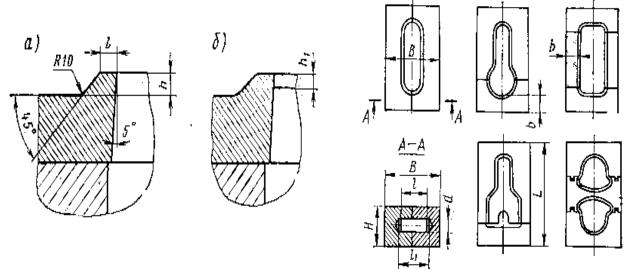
Конструктивные элементы обрезных матриц с острой (а) и тупой (б) режущими кромками
